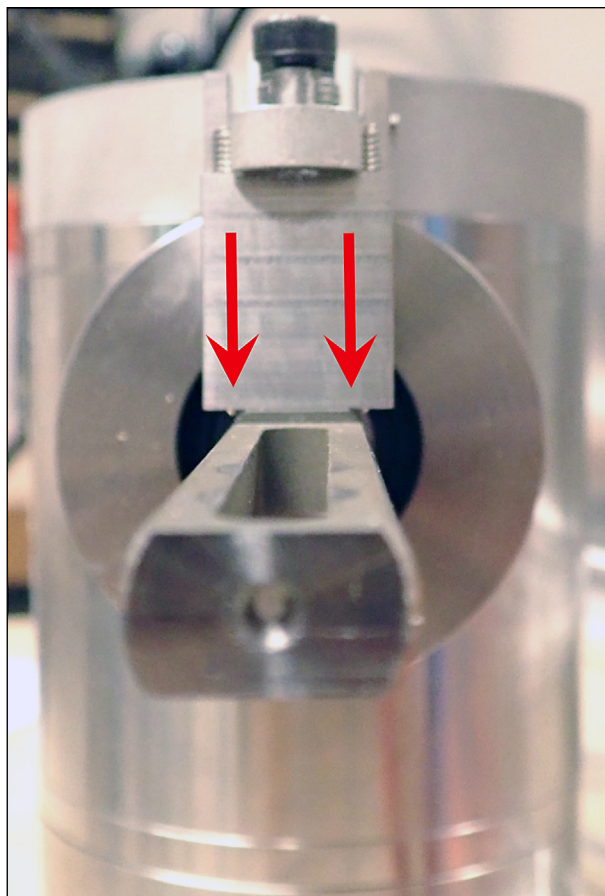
Einbaulehre mit gekennzeichneten Madenschrauben in rot
